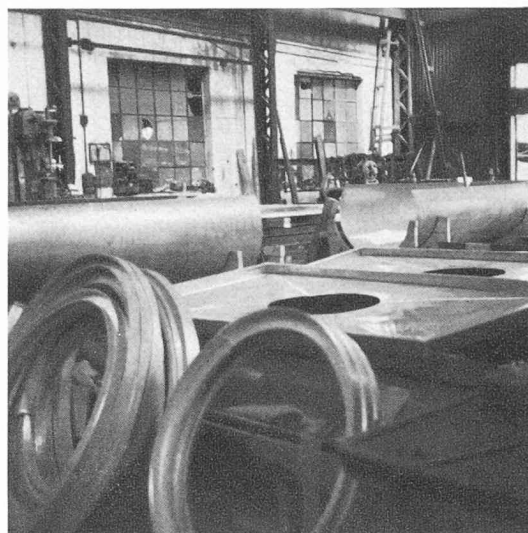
Au premier plan, viroles et planchers des plates-formes supérieures. Au fond, mise en place des trois segments de grand diamètre.
